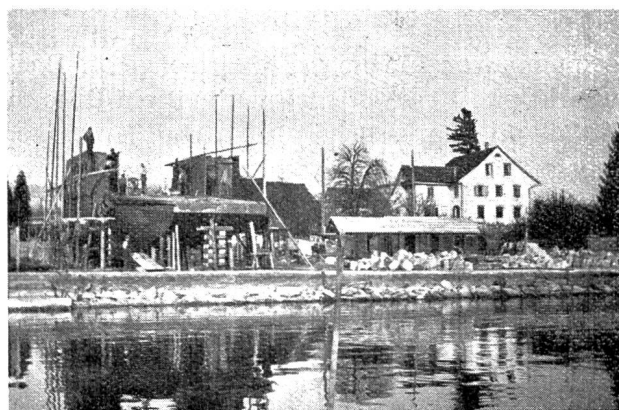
Zürichsee-Fähre Meilen-Horgen. Werftplatz in Obermeilen. Seitennäuser errichtet.
